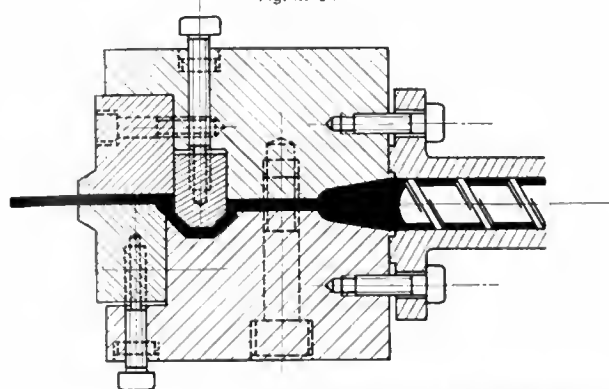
Tête de filière plate pour extrusion de plaques
